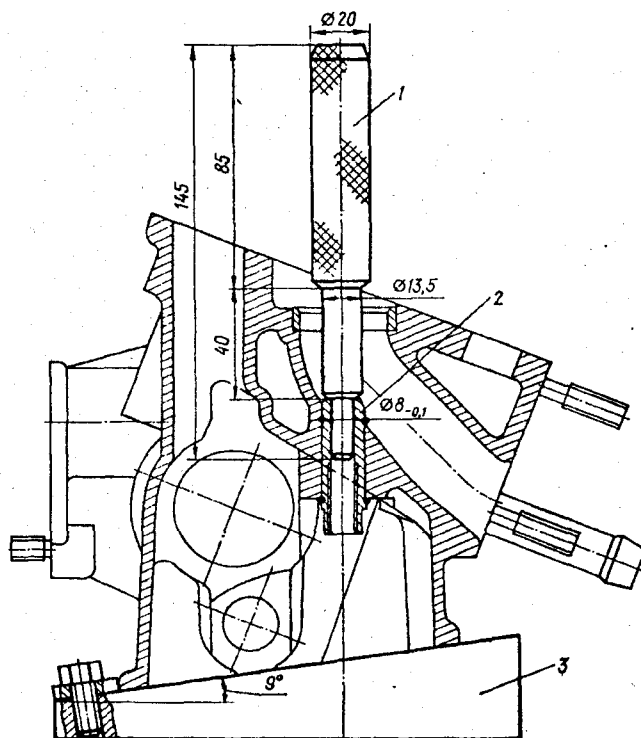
Оправка для выпрессовки направляющей втулки клапана: 1 – оправка; 2 – втулка клапана; 3 – подставка
